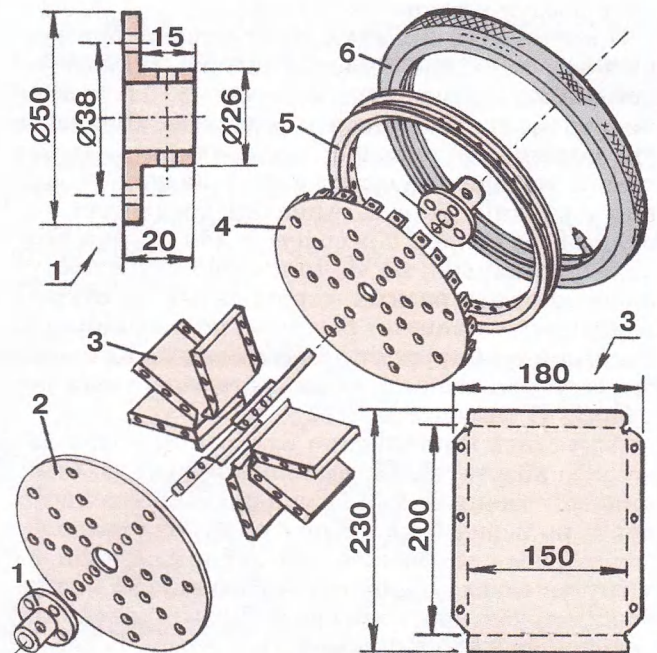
Детали гребного колеса: 1 — фланец; 2 — диск колеса; 3 — гребные лопасти; 4 — опорный диск колеса; 5 — обод велоколеса; 6 — камера с покрывкой.
